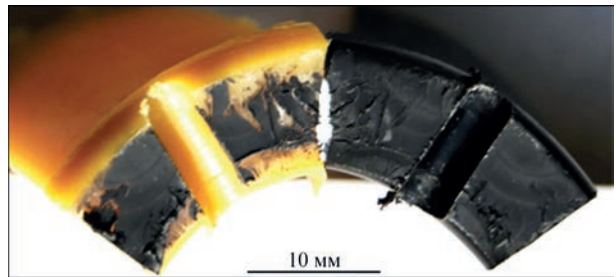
Поверхні руйнування зварного з'єднання труб з ПЕ80 діаметром 110 мм та товщиною стінки 10 мм
